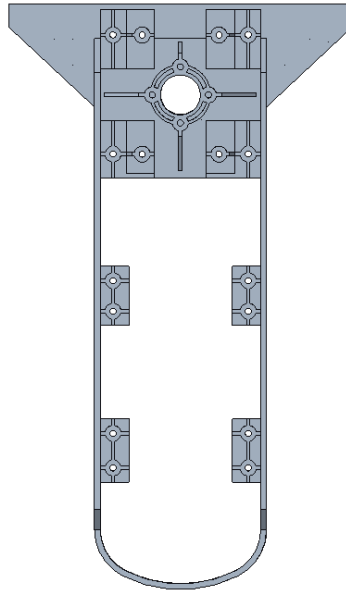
Zonas aprovechadas del concepto columna media de diseño horizontal.
